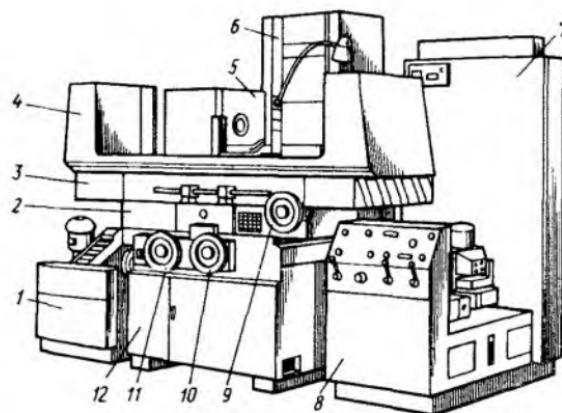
Плоскошлифовальный станок ЗЕ711В:
